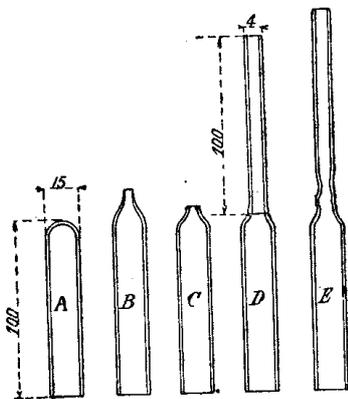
Fabrication d'une ampoule pour tube à vide d'amateur.
